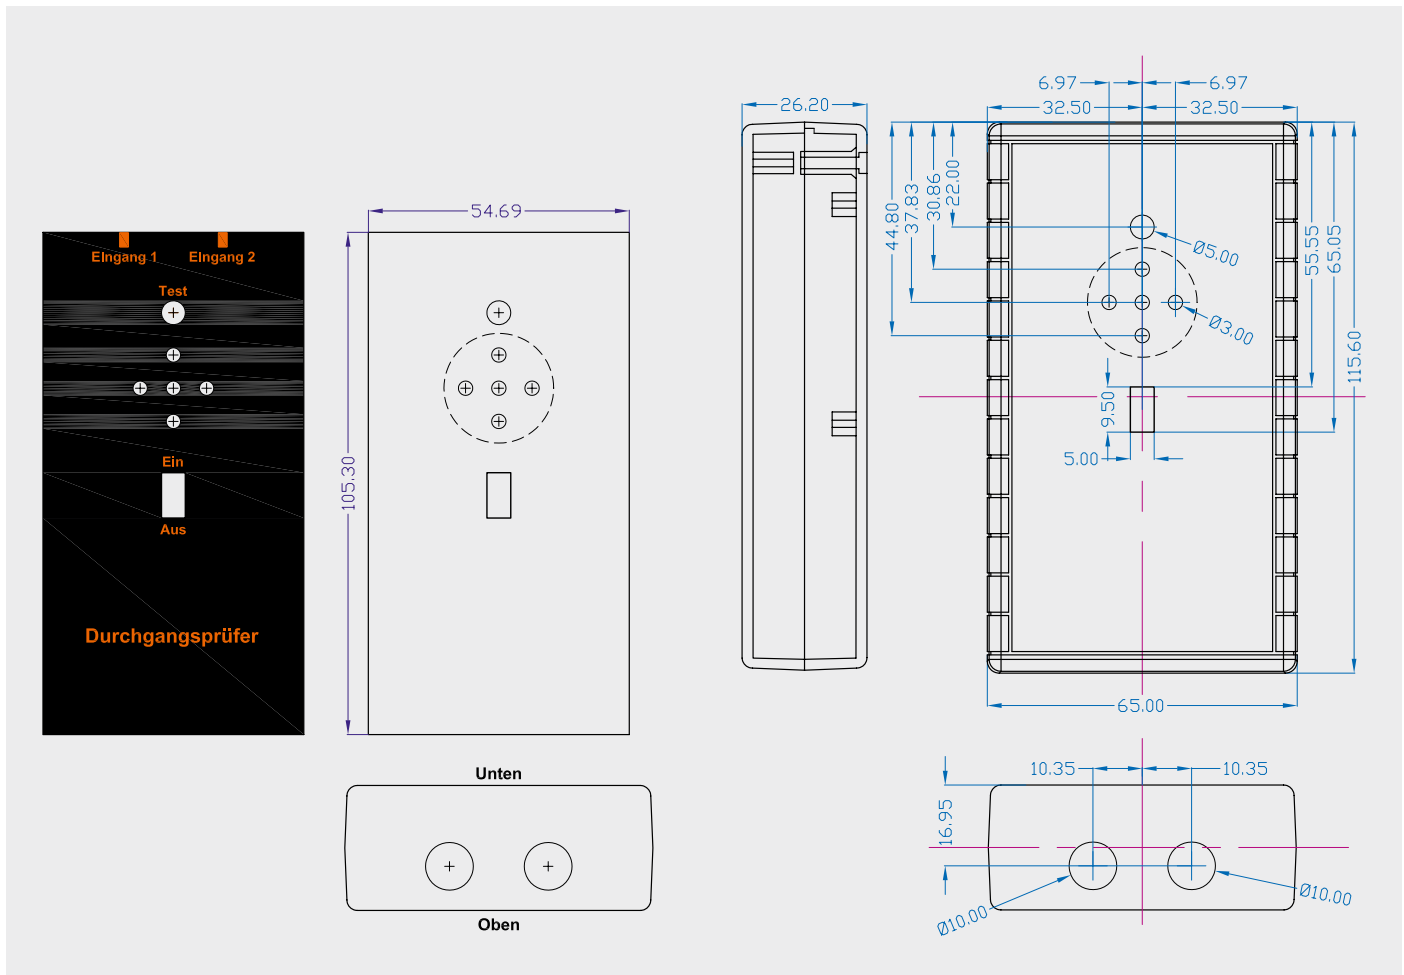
Bohrschablonen und Maßzeichnung für die Gehäuseoberseite und die Frontseite sowie eine Vorlage für das Gehäusedesign mit Beschriftung (verkleinerte Darstellung)
